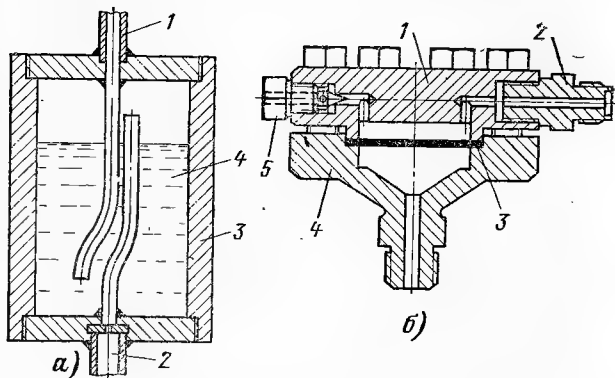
Разделительные устройства для манометров. а — жидкостное; 1 и 2 — трубки; 3 — сосуд; 4 — разделительная жидкость; б — мембранное; 1 — крышка; 2 — штуцер; 3 — резиновая мембрана; 4 — корпус; 5 — пробка.
